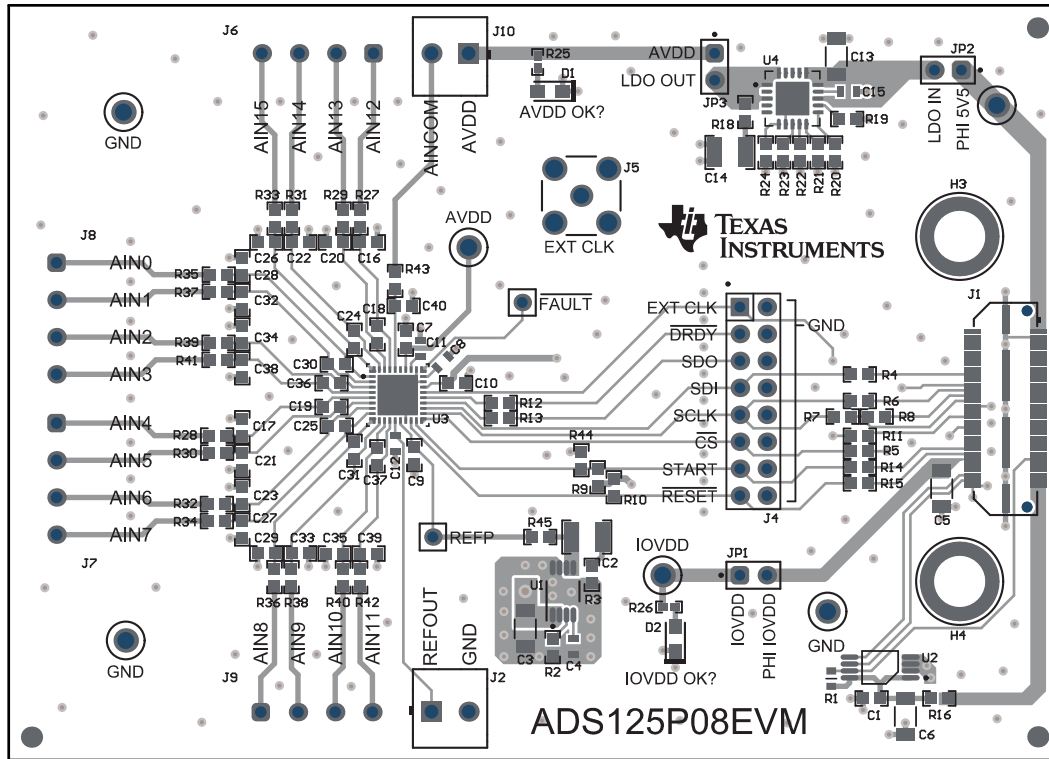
ADS125P08 EVM PCB 布局 — 顶层
